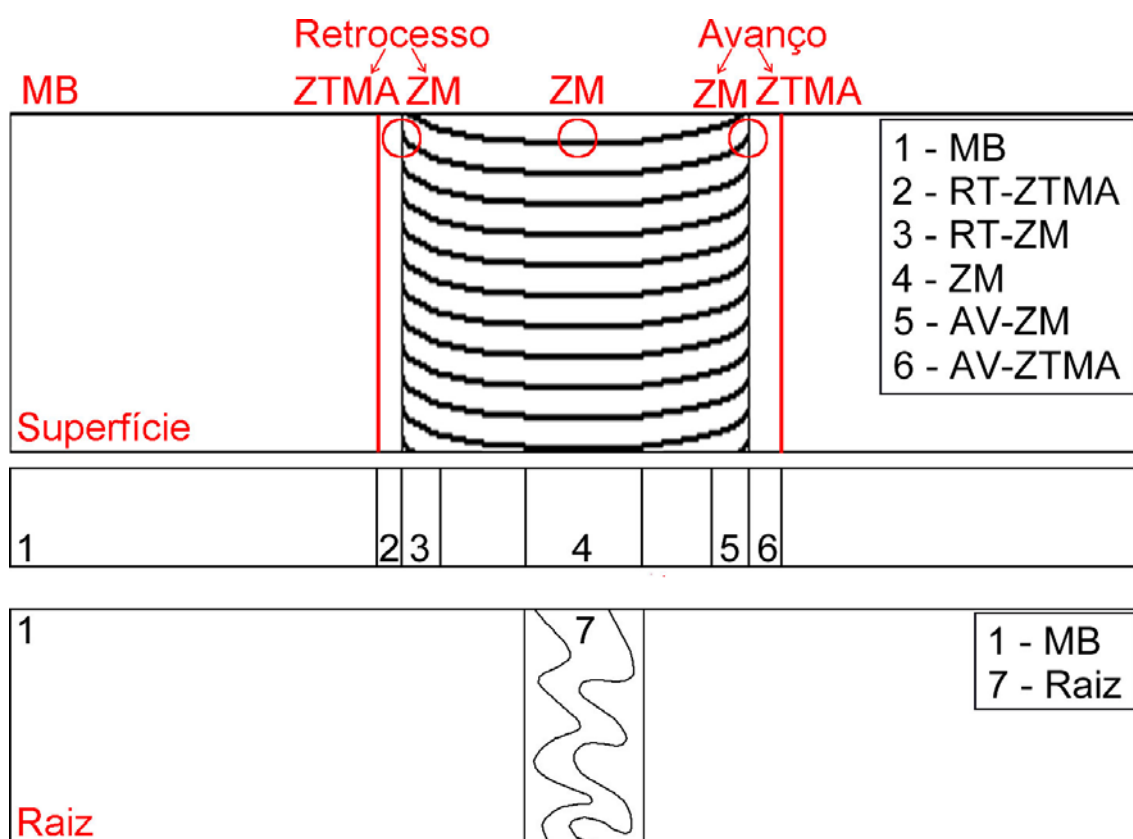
Desenho esquemático da junta soldada com a identificação das regiões soldadas.
